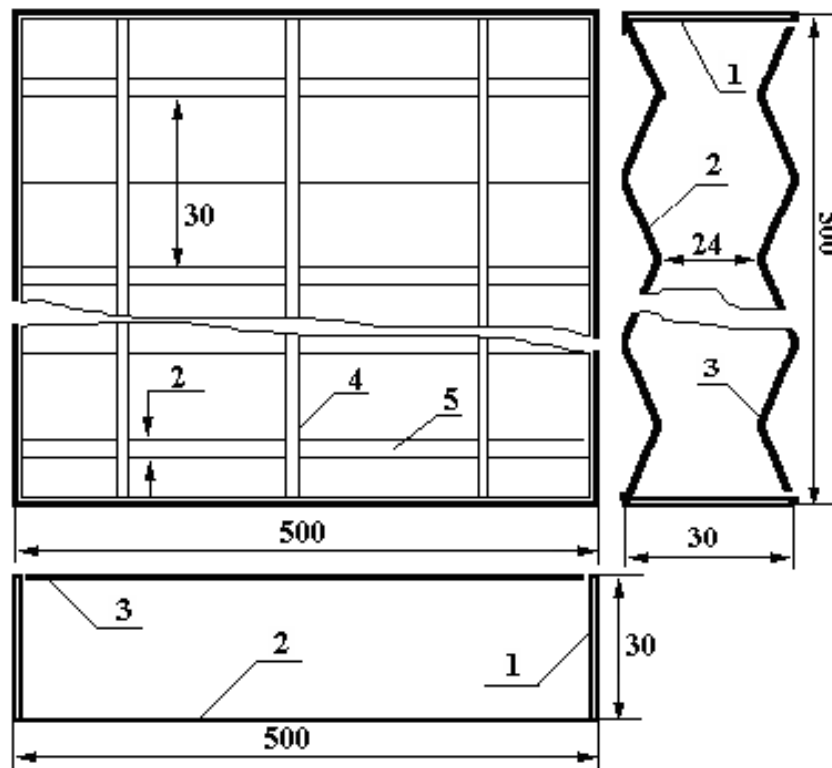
ФЄ з плаваючою кришкою: 1 – обичайка; 2 – дно; 3 – плаваюча кришка; 4 – пластини твердості; 5 – масообмінні зазори
